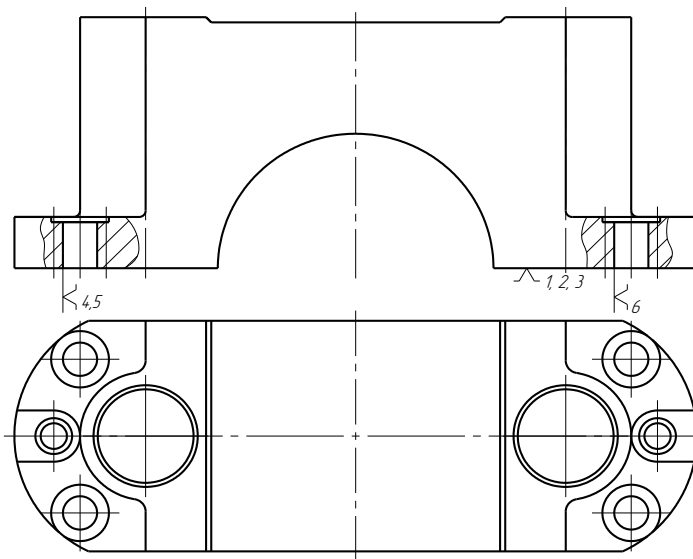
Теоретична схема базування деталі корпус
